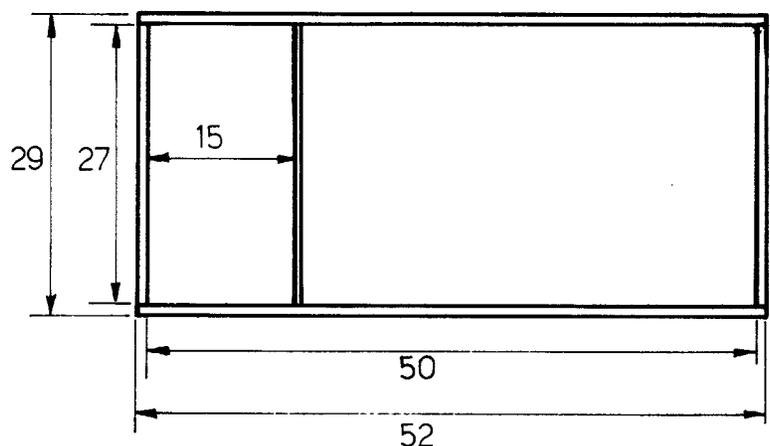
Disposizione del fondo e delle quattro pareti.
